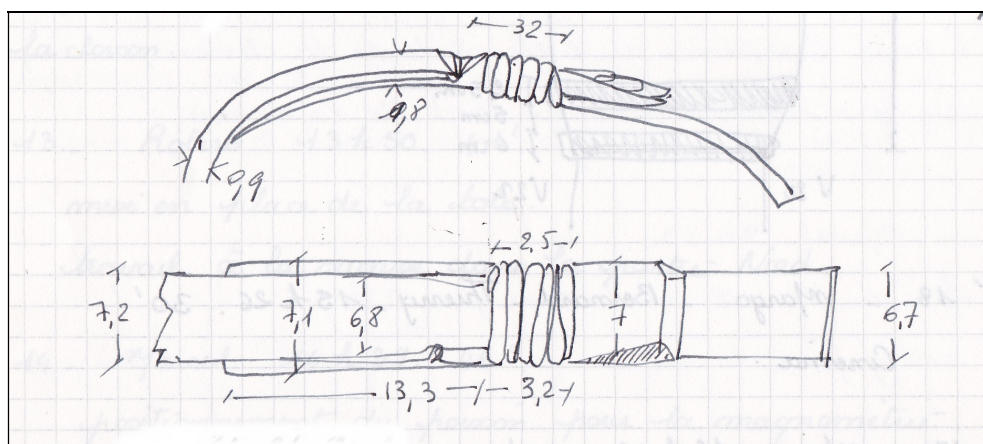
Ligature type 1 du baril A 334 (dessin M.G.)
